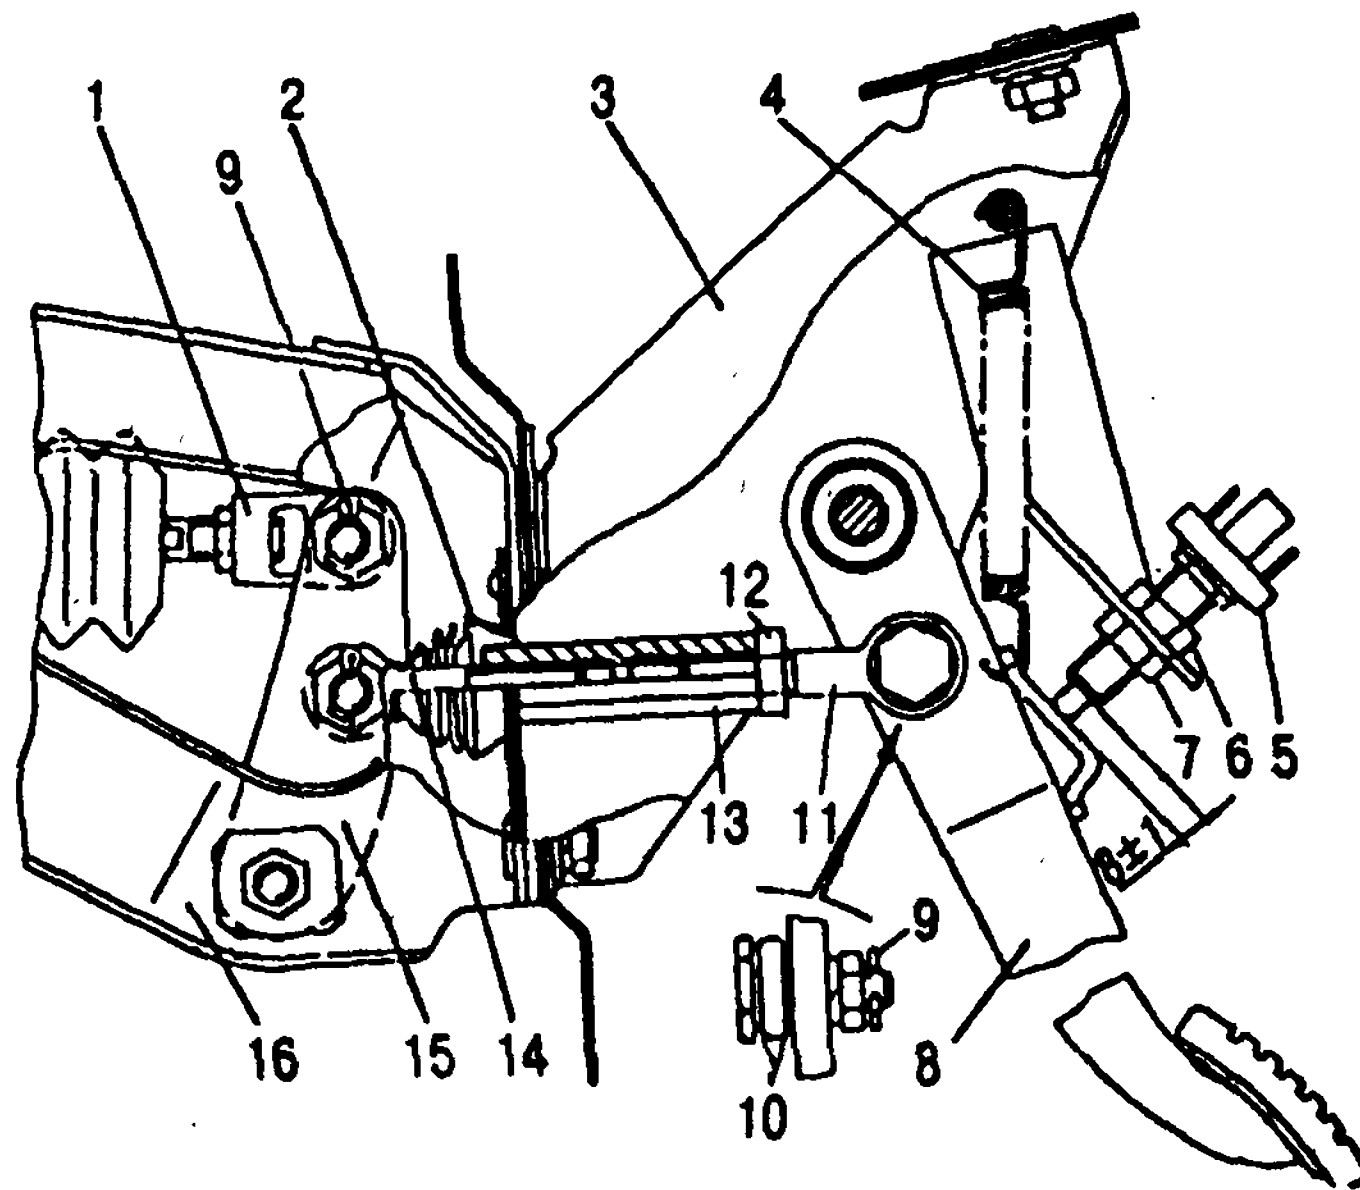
Педали рабочих тормозов: 1 - проушина; 2 - чехол; 3 - кронштейн педалей; 4 - пружина; 5 - выключатель сигнала торможения; 6, 7 и 12 - гайки; 8 - педаль; 9 - шплинт; 10 - пластмассовые втулки; 11 и 14 - резьбовые стержни; 13 - муфта; 15 - рычаг; 16 - кронштейн вакуумного усилителя
